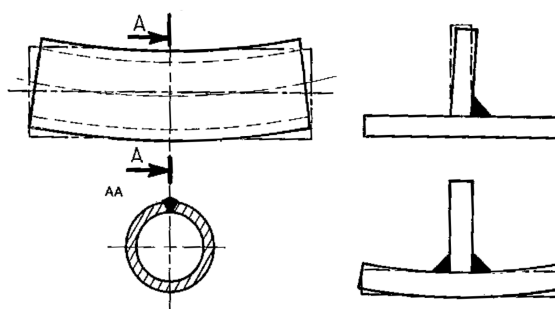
Exemplos de deformações registadas em peças soldadas. Adaptada de [Q1]
